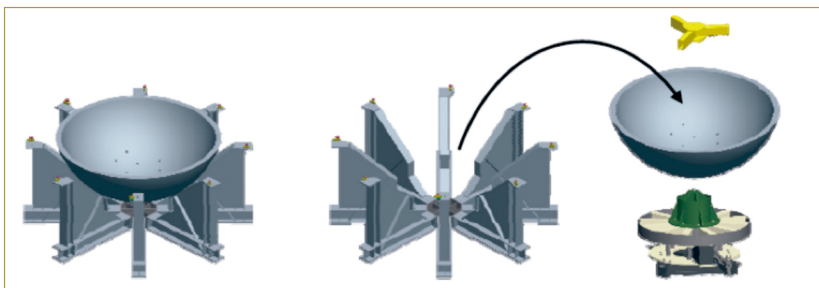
Traslado del fondo de la vasija a la mesa giratoria.
